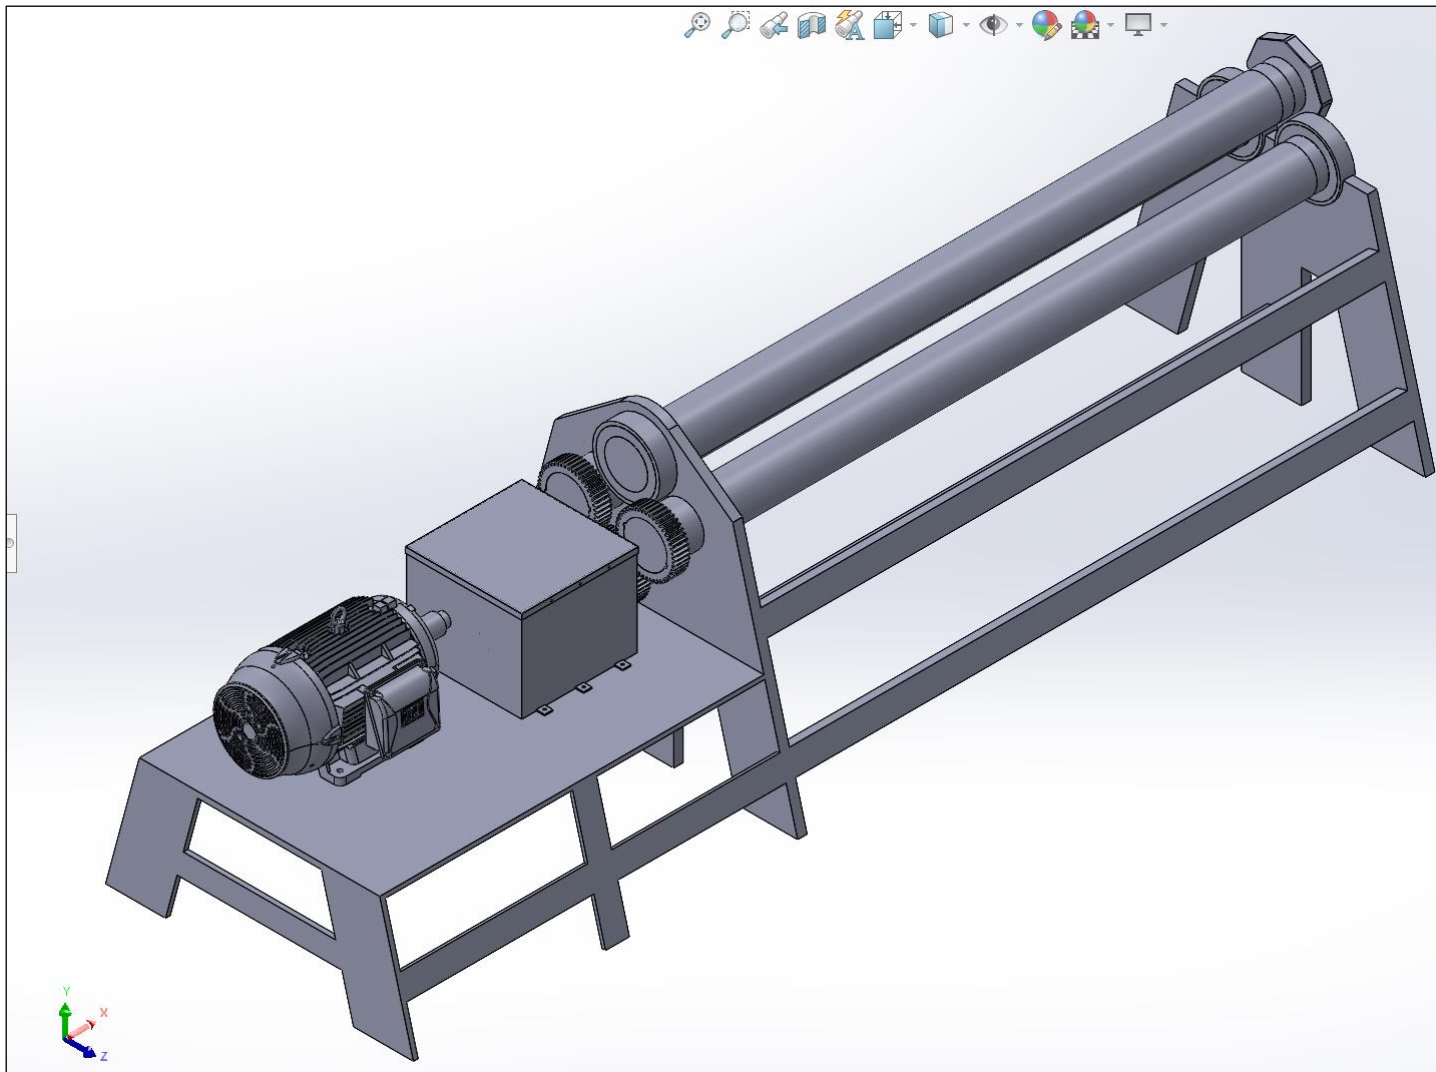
Ensamblaje de los componentes para la máquina roladora.
